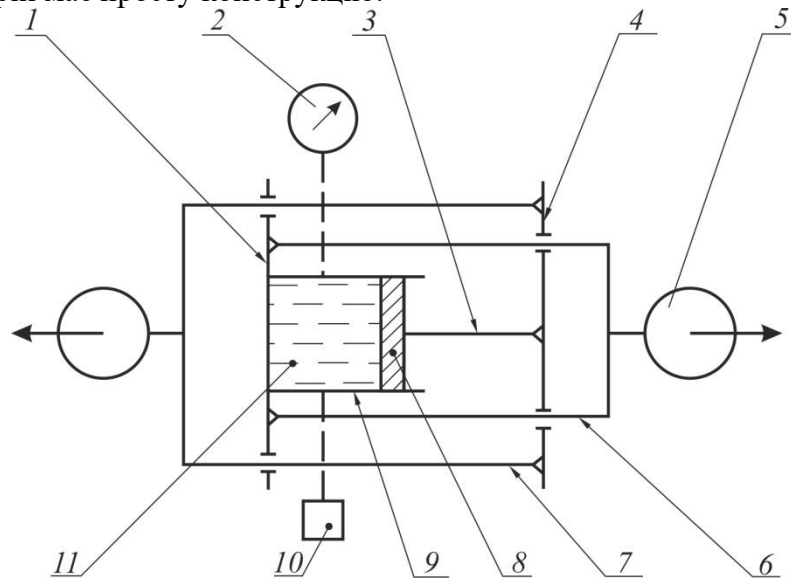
Гідромеханічний пристрій для вимірювання сили тяги на гаку трактора:
